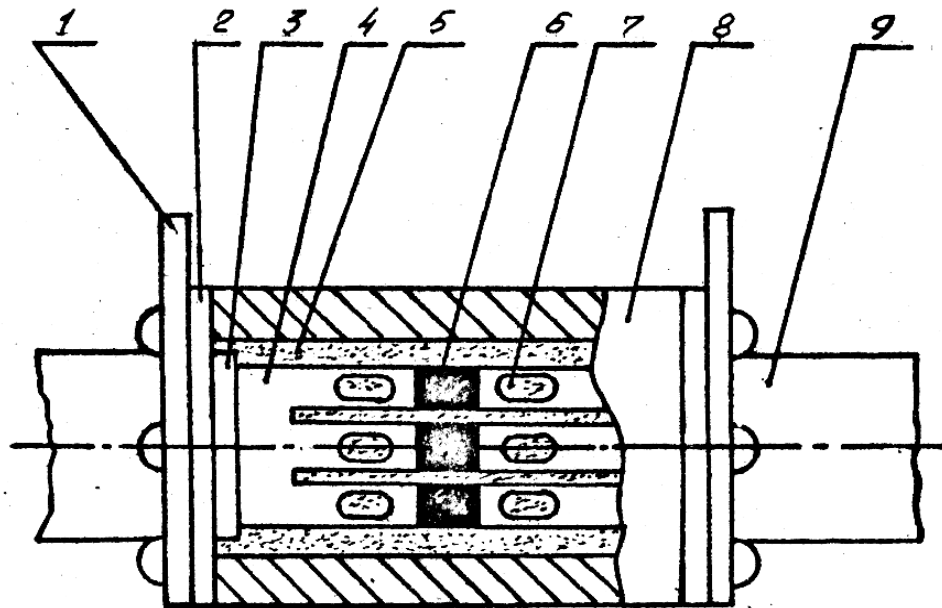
Запобіжник типу ПН-2 :1- кришка; 2- азбестова прокладка; 3- прокладка; 4- плавка вставка; 5- кварцевий пісок; 6 – олов'яна напайка; 7- просічка; 8- корпус; 9- врубний контакт виводу.
